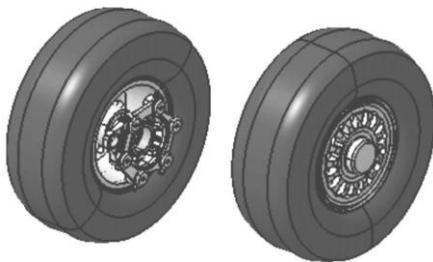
Колеса основных опор шасси в сборе с шиной
